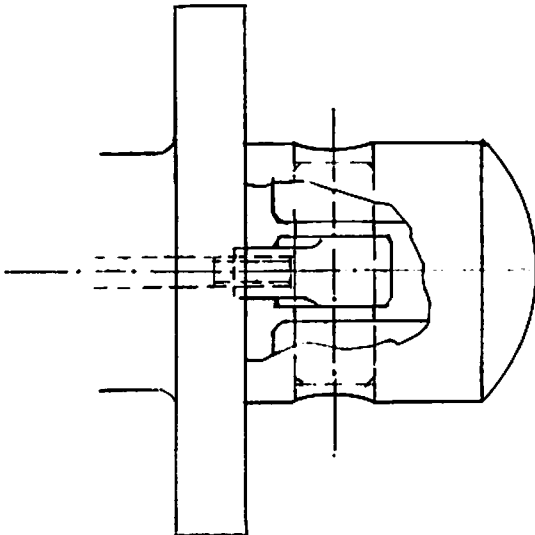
Aufspannen des Kolbens zur Bearbeitung der Kolbenbolzenbohrung.
